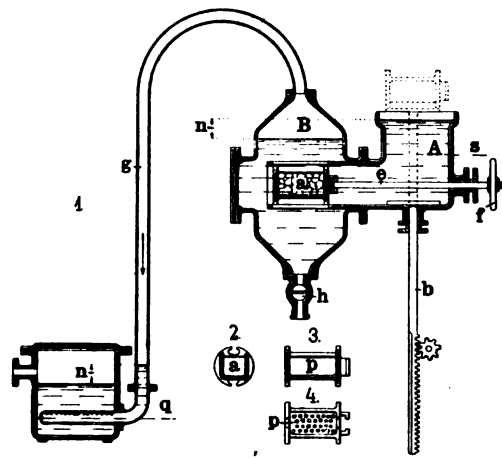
Z. A.: Die Acetylenleuchtungs-Anlage in Lichtensteil (Schweiz).
